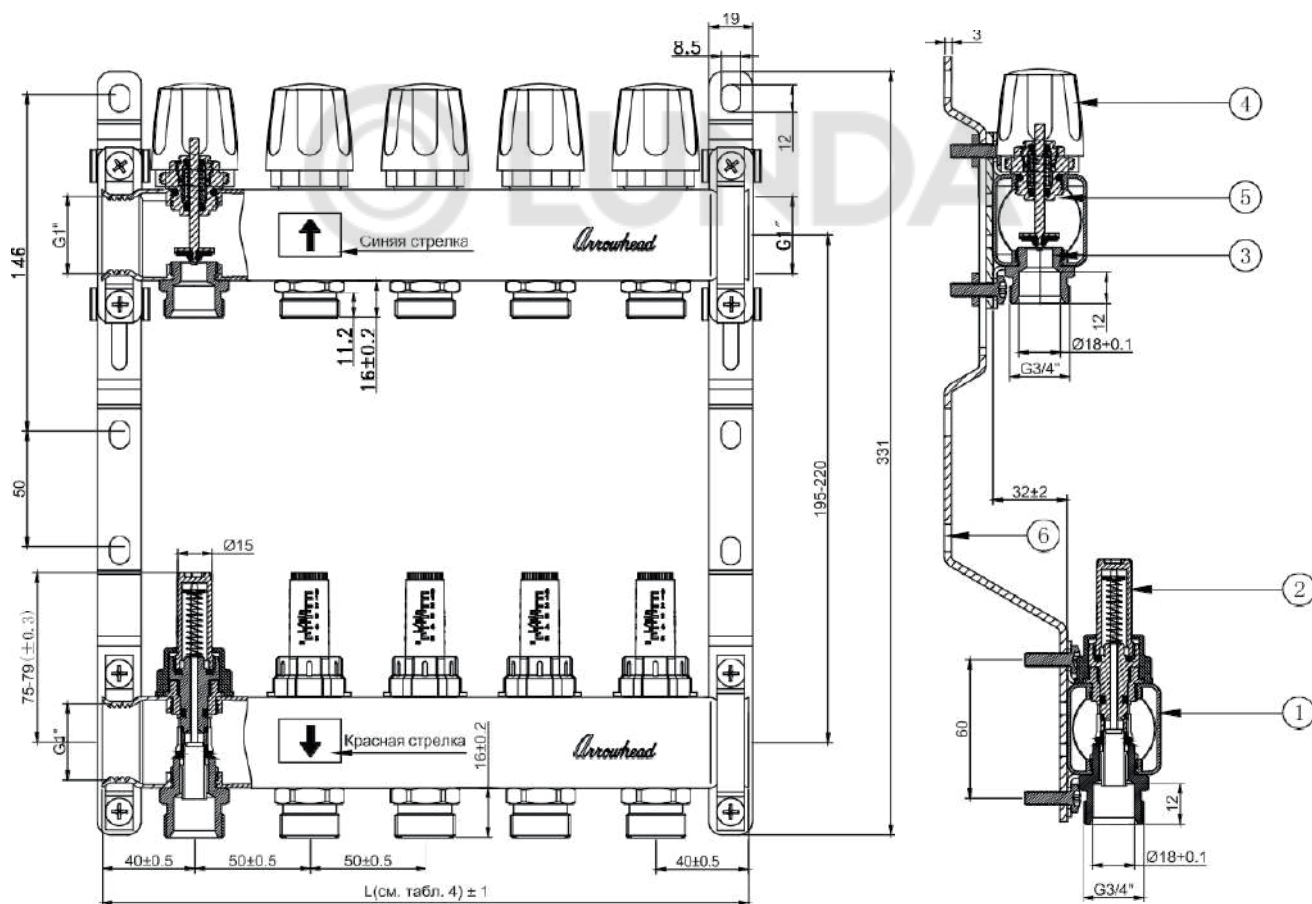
Основные детали и габариты коллекторов серии CS-500-xx ARROWHEAD
